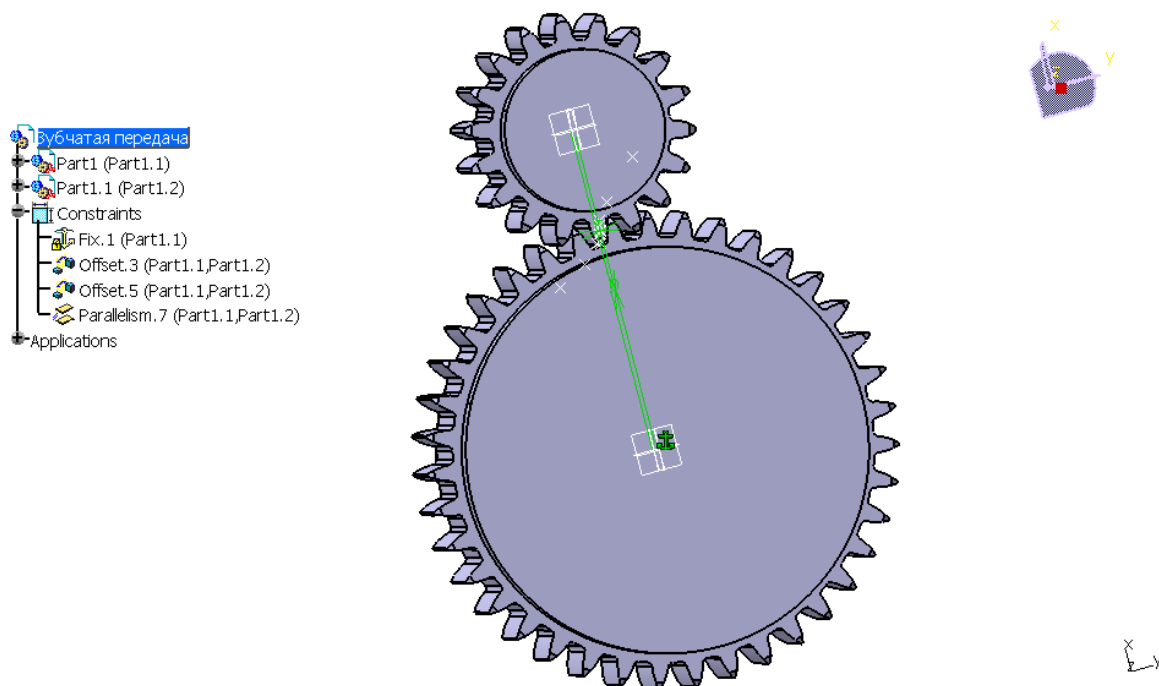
Результат сборки двух зубчатых колес.
